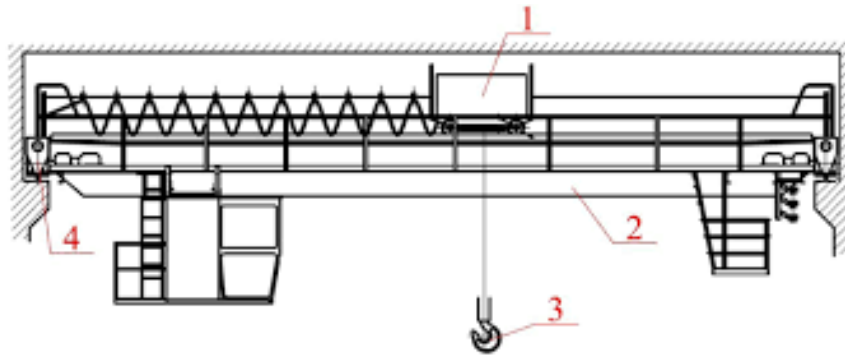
Приципова схема роботи мотсового крана: 1– вантанжий візок (механізм підйому для вертикального переміщення вантажу); 2 – механізм пересування візка для переміщення вантажу в горизонтальній площині по одній осі; 3 – вантанжий гак; 4 – механізм пересування крана для переміщення вантажу у горизонтальній площині по іншій осі.
